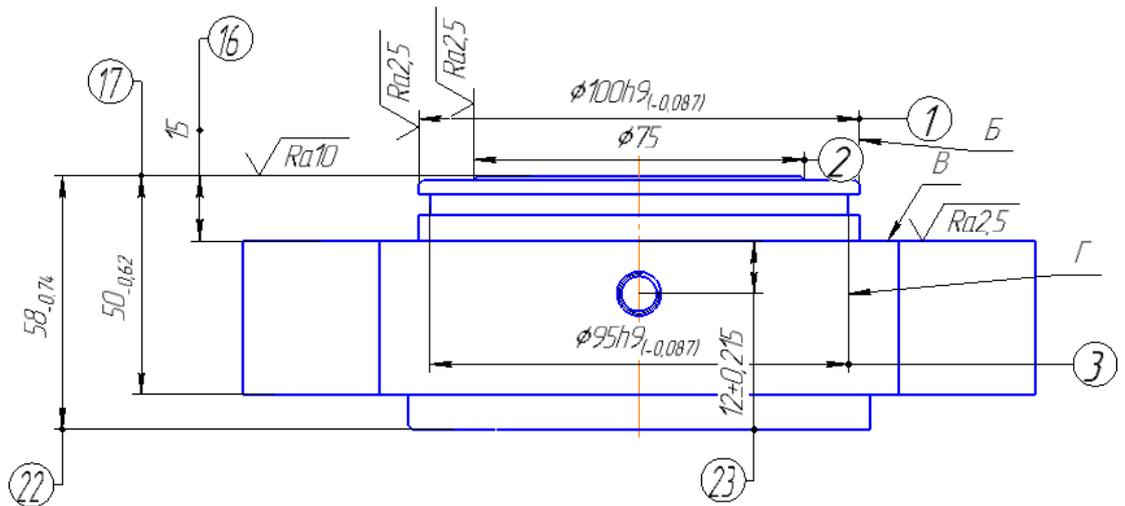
Вид сверху по чертежу. Нумерование поверхностей детали
